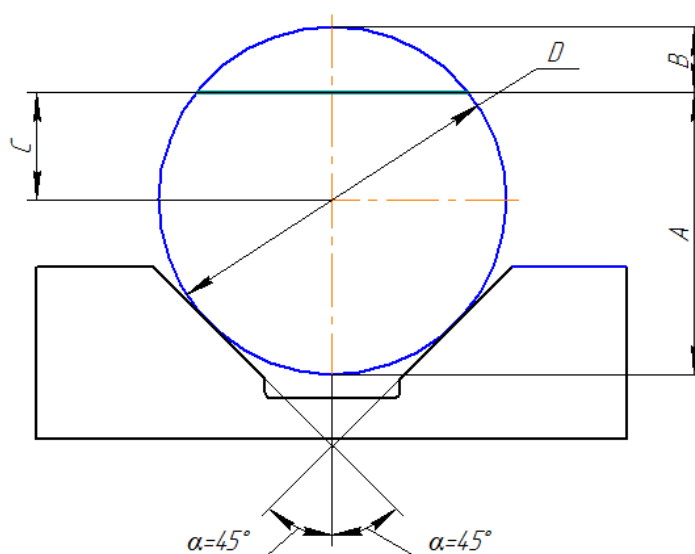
Способи задання розміру фрезерованої лиски
